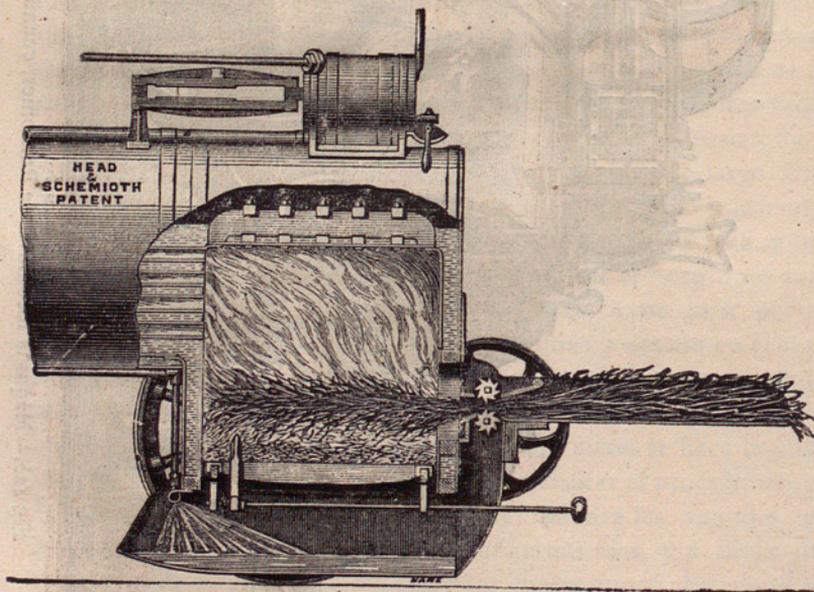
Seccion longitudinal del hornillo de la locomóvil.
